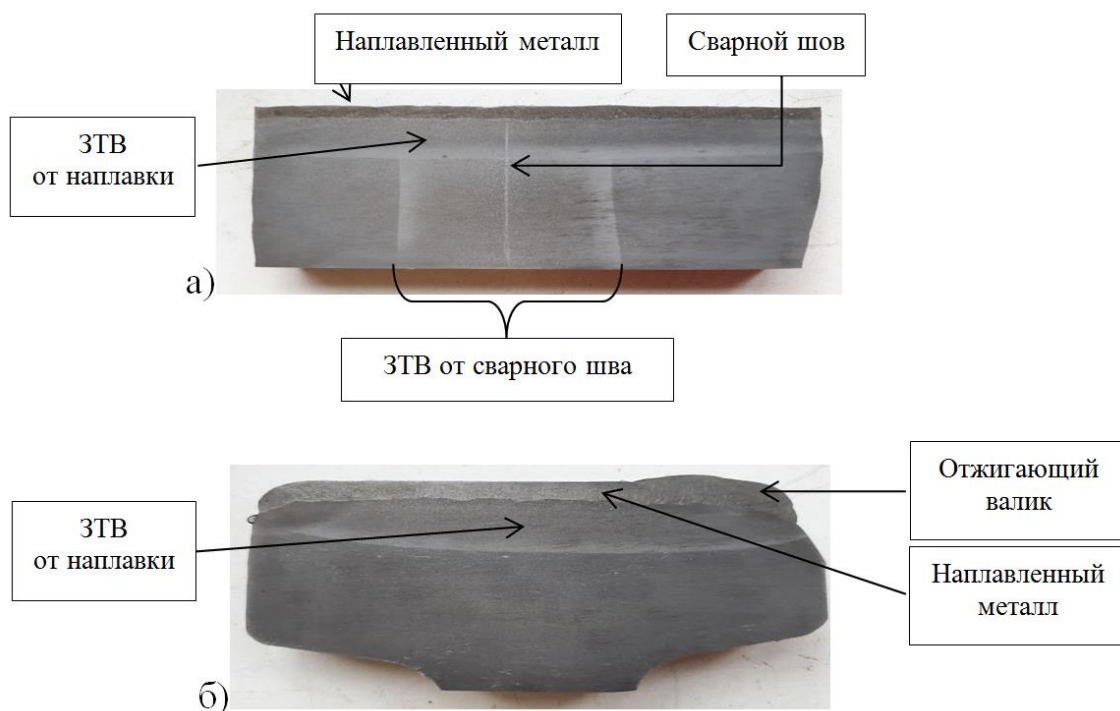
Макроструктура сварного соединения рельса, наплавленного в один слой: а) – продольный шлиф; б) – поперечный шлиф
